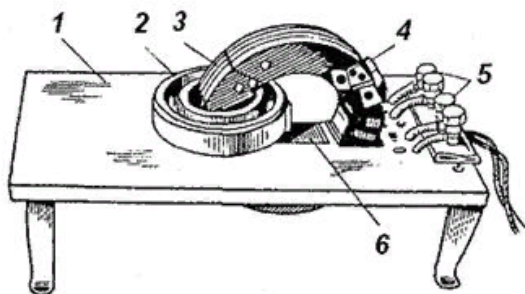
Приспособление для индукционного нагрева подшипников при посадке на вал двигателя
